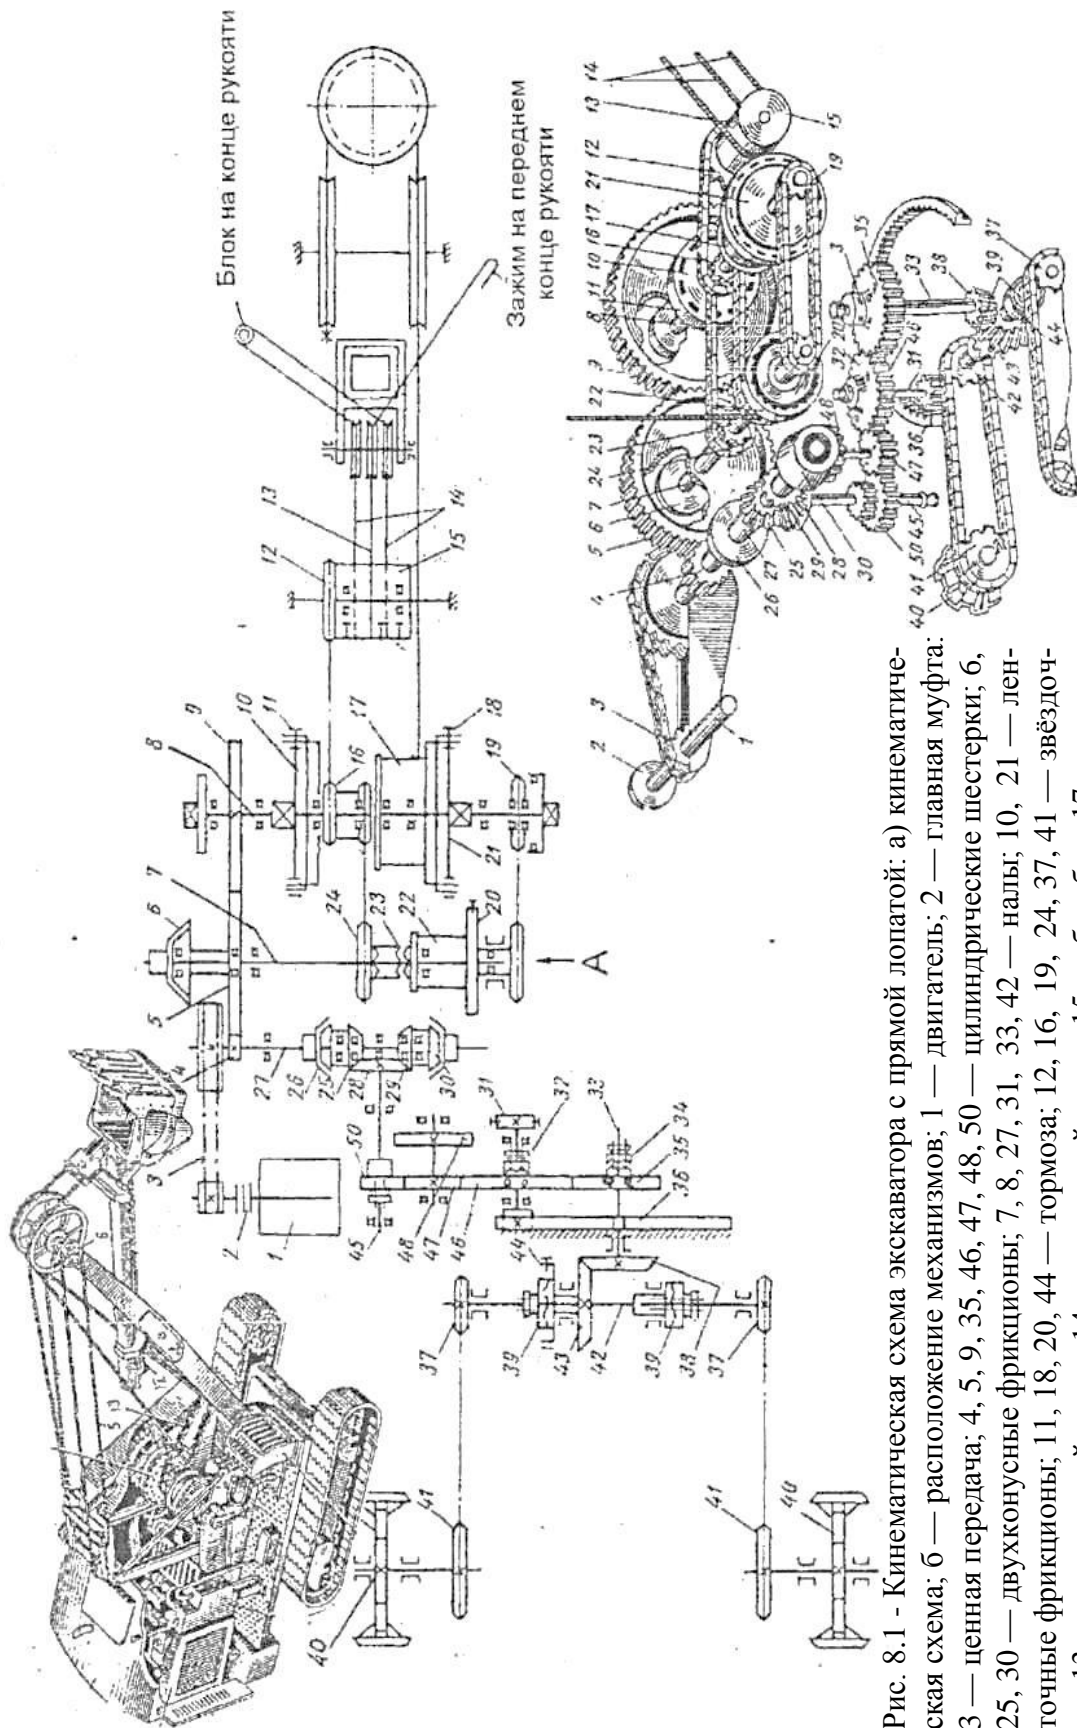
Кинематическая схема экскаватора с прямой лопатой: а) кинематическая схема; б — расположение механизмов; 1 — двигатель; 2 — главная муфта; 3 — центная передача; 4, 5, 9, 35, 46, 47, 48, 50 — цилиндрические шестерни; 6, 25, 30 — двухконусные фрикционы; 7, 8, 27, 31, 33, 42 — валы; 10, 21 — ленточные фрикционы; 11, 18, 20, 44 — тормоза; 12, 16, 19, 24, 37, 41 — звездочные фрикционы; 13 — возвратный канат; 14 — напорный канат; 15 — барабан; 17 — подъемный барабан; 22 — стрелоподъемный барабан; 23, 32, 34, 39 — кулачковые муфты; 25, 28, 29, 38, 43 — конические шестерни; 36 — зубчатый венец; 40 — ведущие звездочки гусениц; 45 — вертикальный вал реверса.
